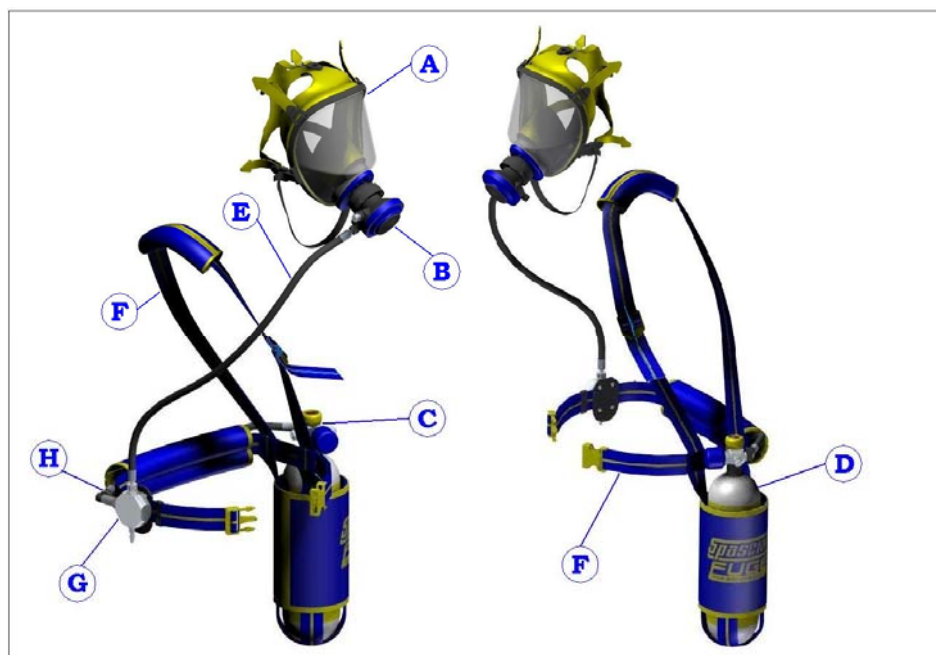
Dispositivo FUGE TAIL – Vista d'assieme
